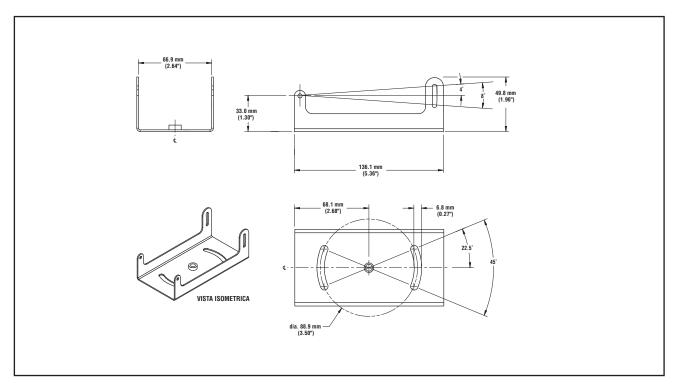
Staffa di montaggio sensore assiale - Dimensioni
